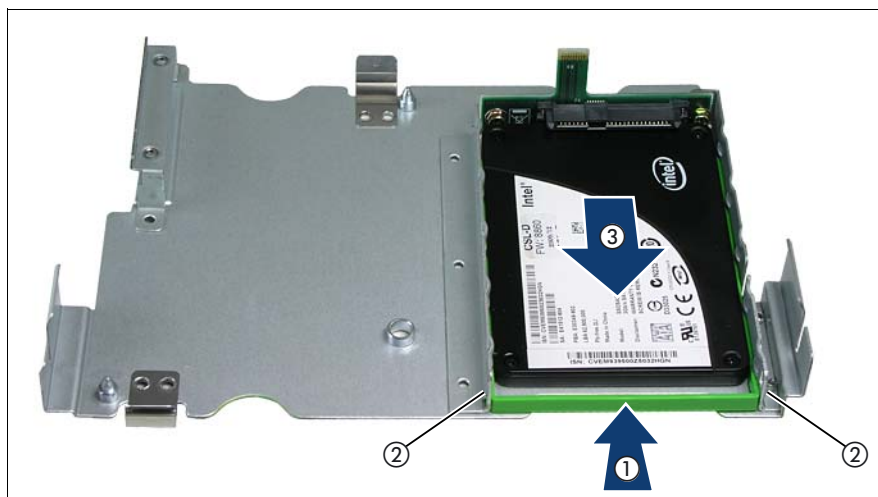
Einbaurahmen der SSD-Laufwerk entfernen.
